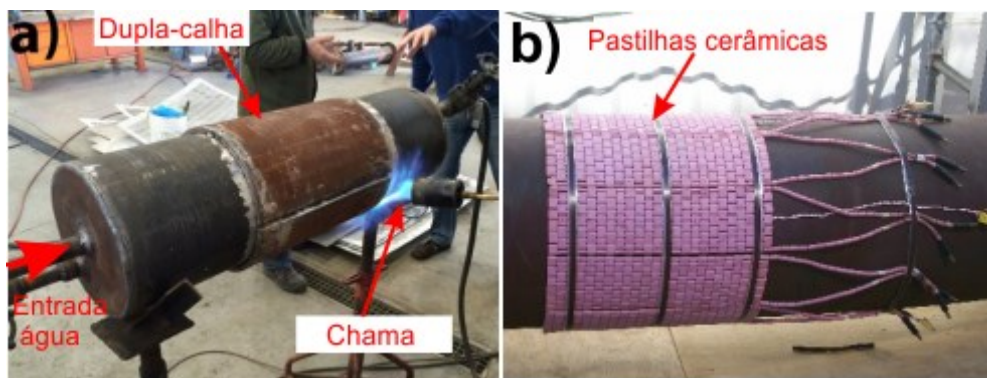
Em a) aquecimento de soldagem em operação por chama; b) aquecimento de soldagem em operação por condução. Adaptado de Yunovich e Thompson [7].
